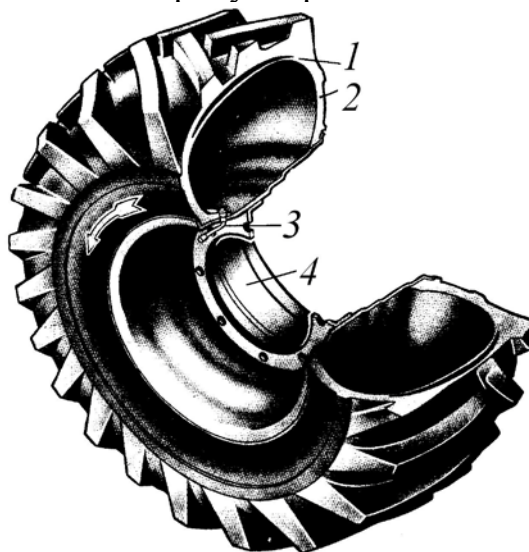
Колесо трактора общего назначения: 1 – покрышка; 2 – камера; 3 – вентиль; 4 – диск
